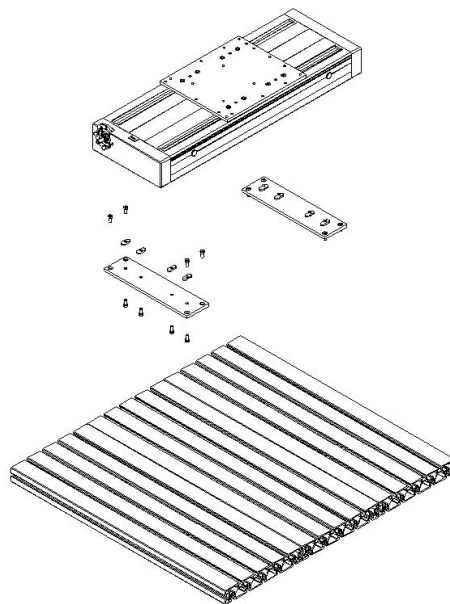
Handlingsystem iLE 20/20 für die Fußmontage
